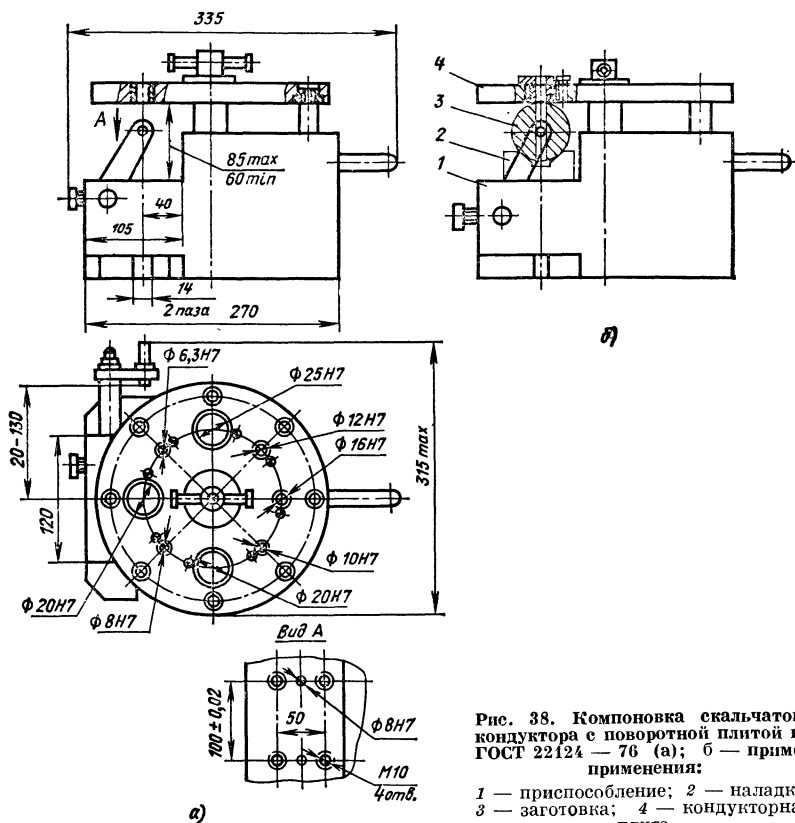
Компоновка скальчатого кондуктора с поворотной плитой по ГОСТ 22124 — 76 (а); б — пример применения:
